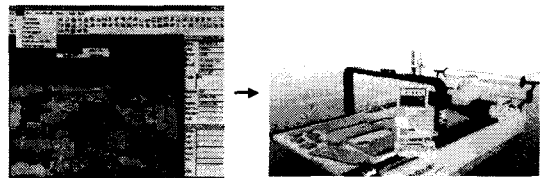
마커메이킹시스템과재단기계(cutting machine)
